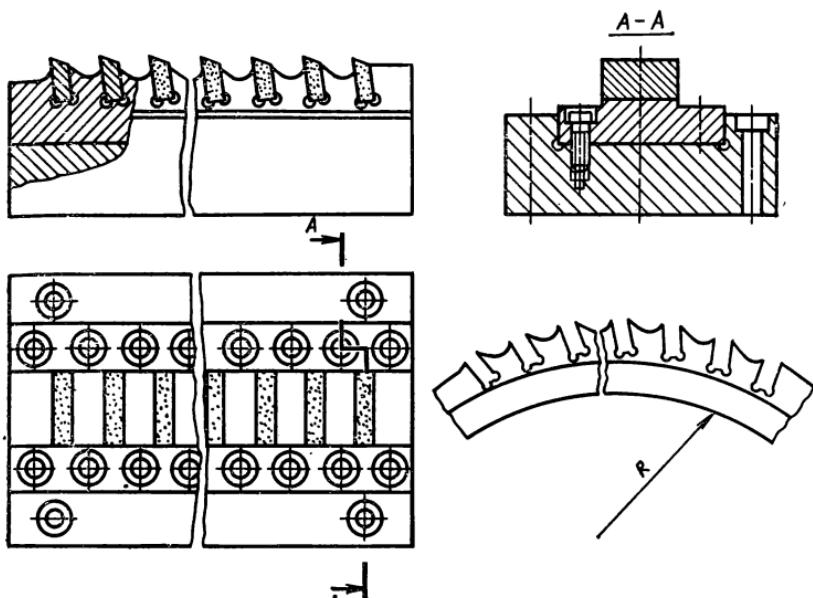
Сборная твердосплавная протяжка с креплением зубьев-пластин силами упругой деформации
